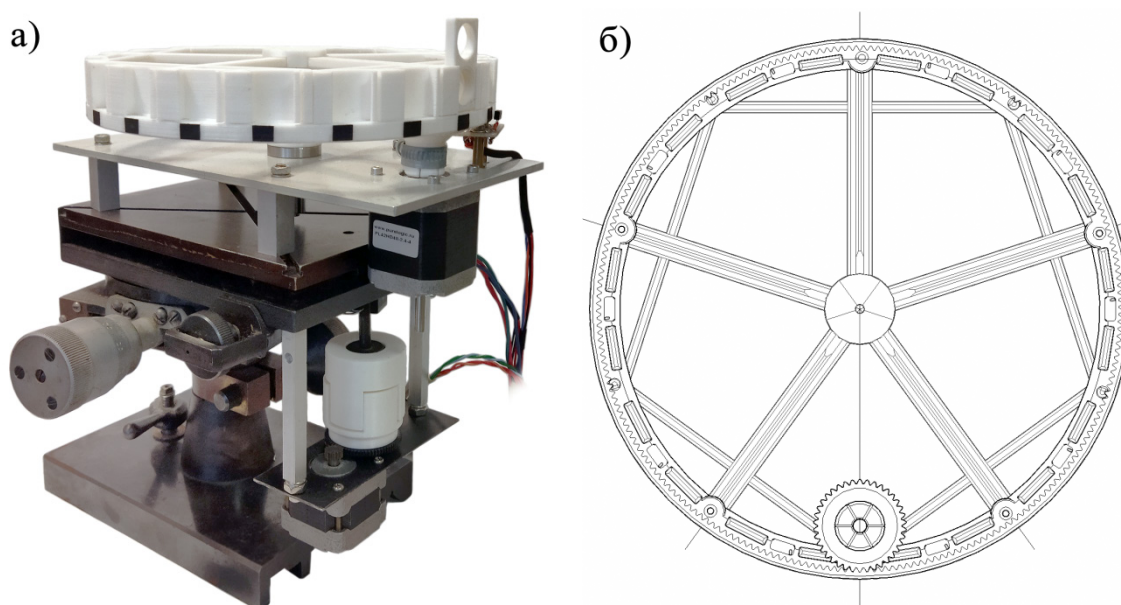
Узел перемещения образцов в лазерном стенде (а) с сборной зубчатой передачей (б)
